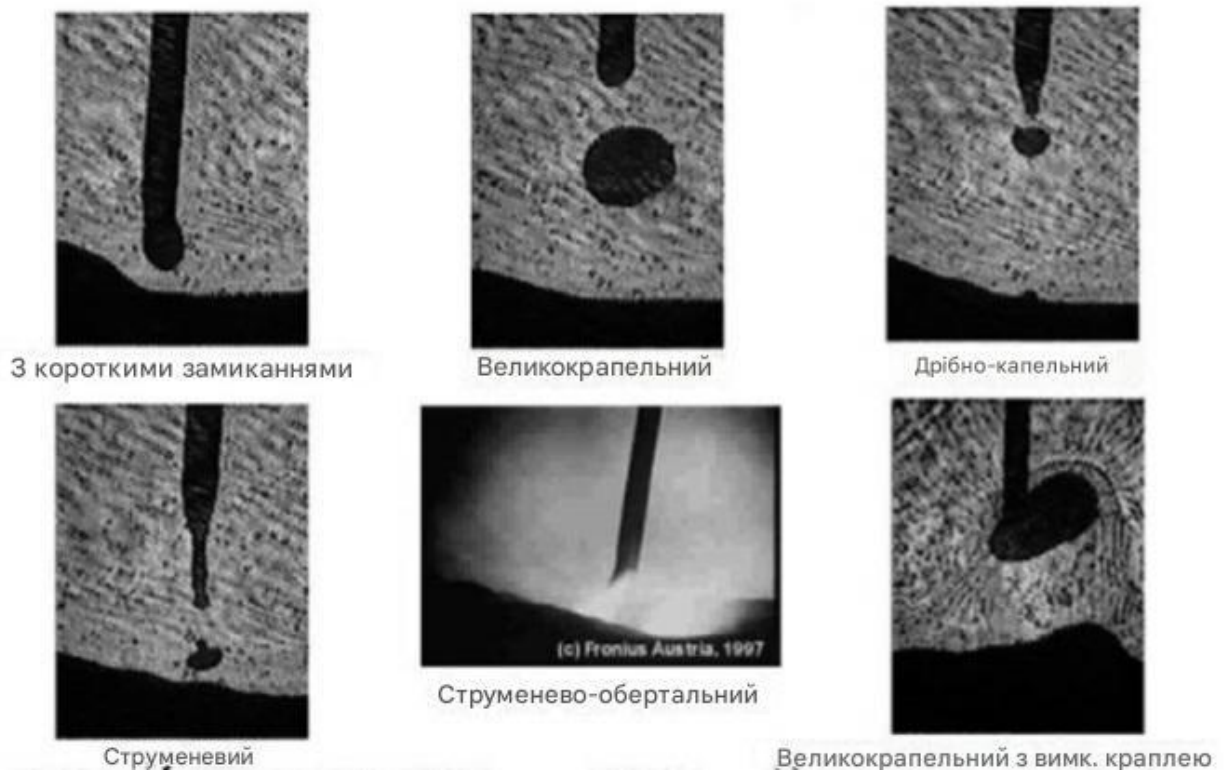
Принципові способи переносу металу в умовах автоматизованого зварювання.
